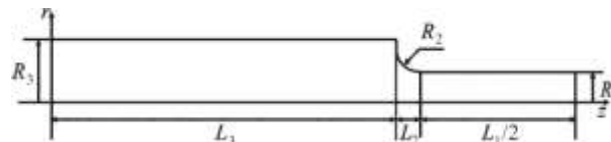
Конструктивная схема образца с цилиндрической рабочей частью
